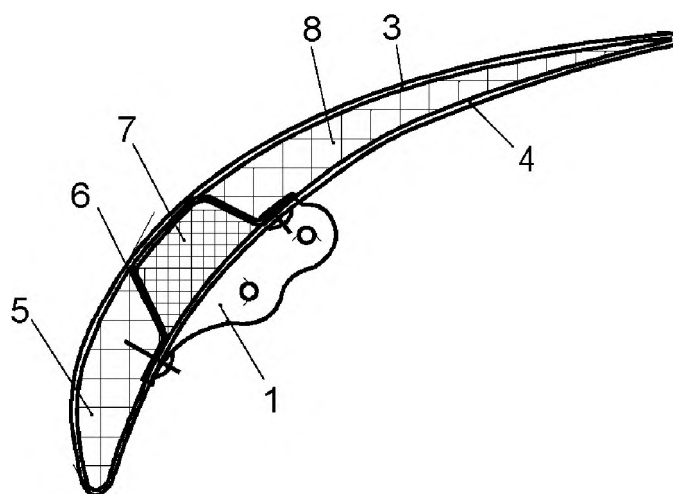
Конструкция предкрылка оперения Ка-226А из ПКМ [12]:
